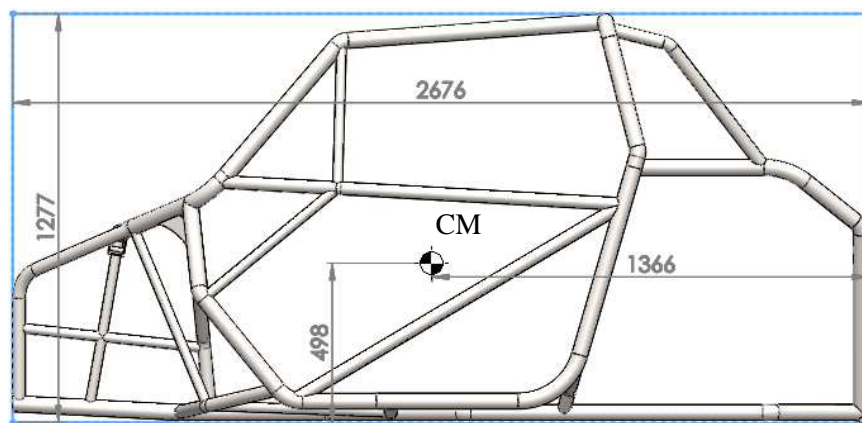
Centro de massa e dimensões gerais do chassi de competição projetado
